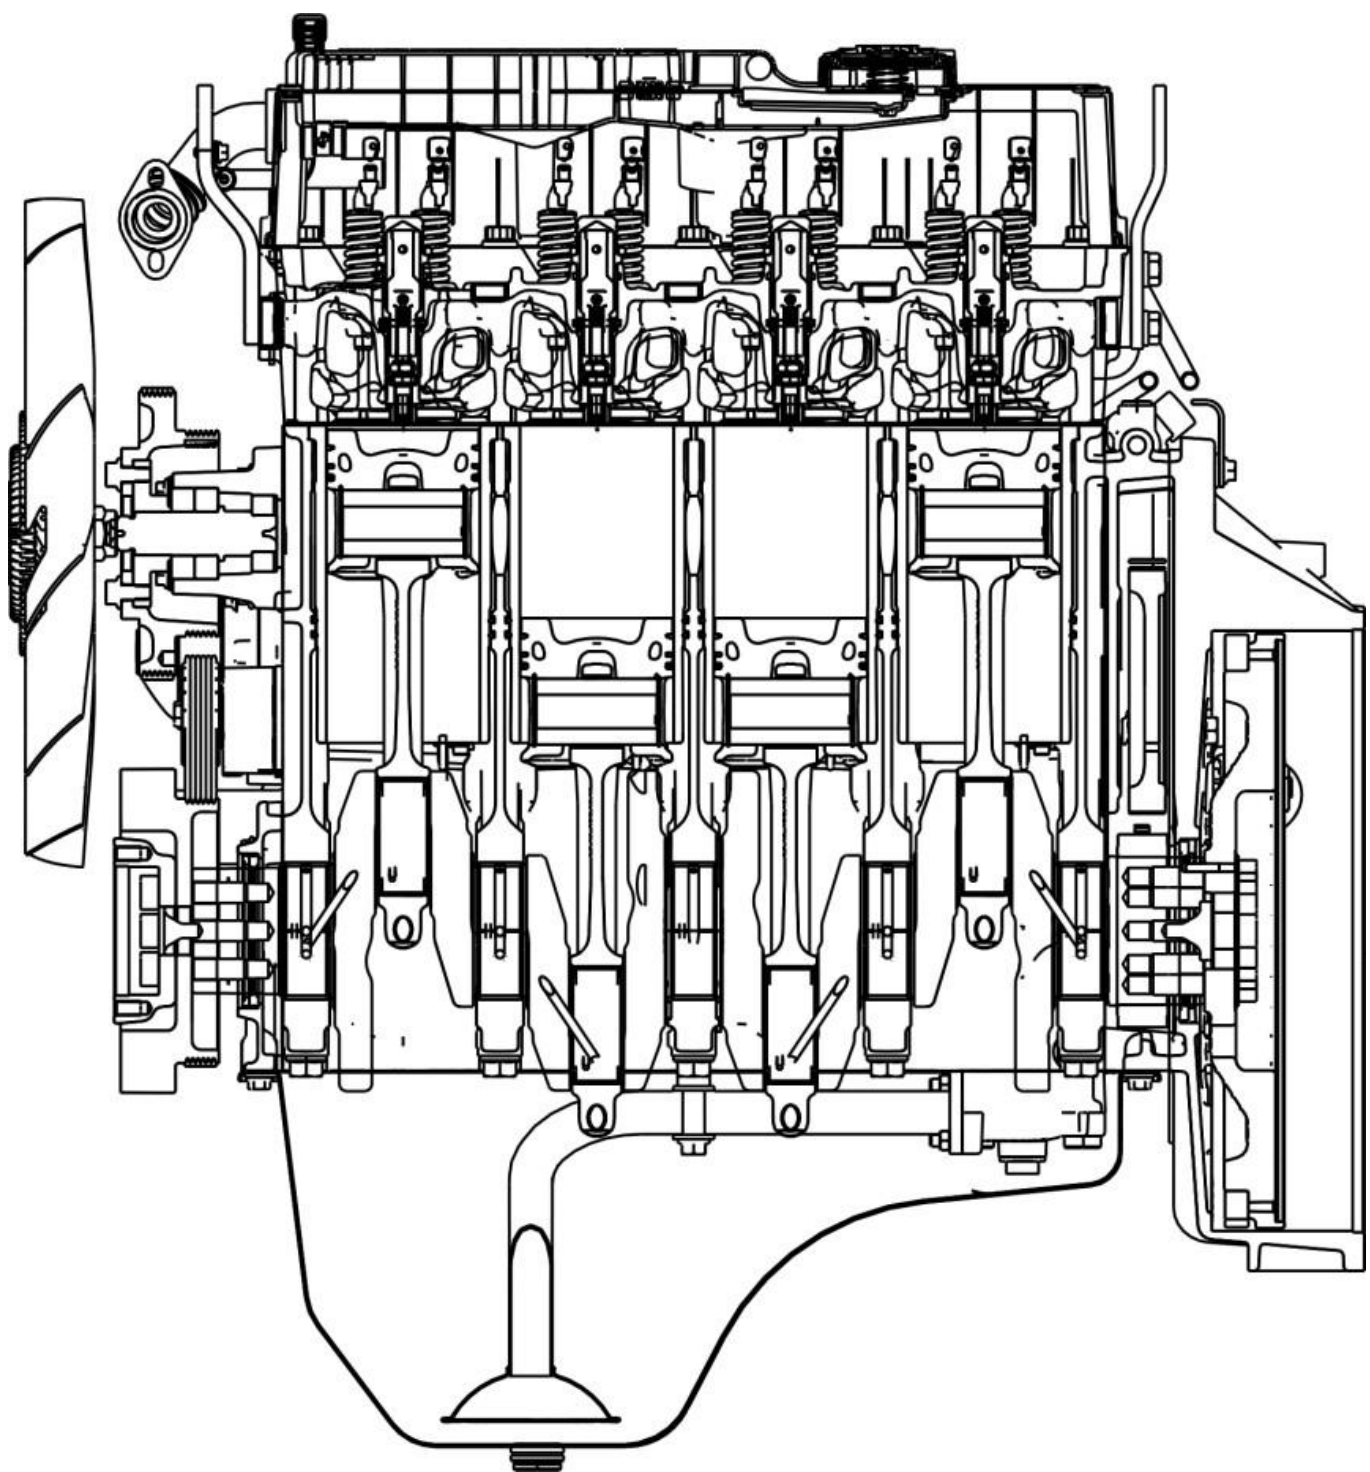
Продольный разрез двигателя ЯМЗ-53444-20
